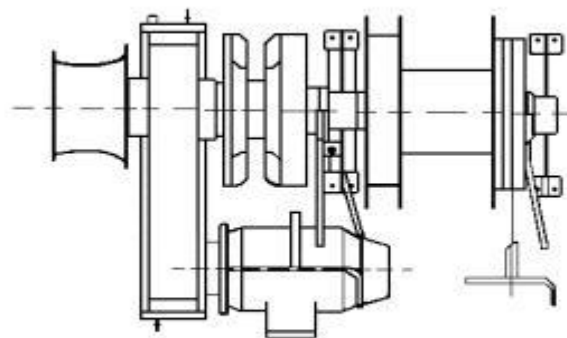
Якорно-швартовная лебедка (полубрашпиль с швартовным барабаном). Схема.
